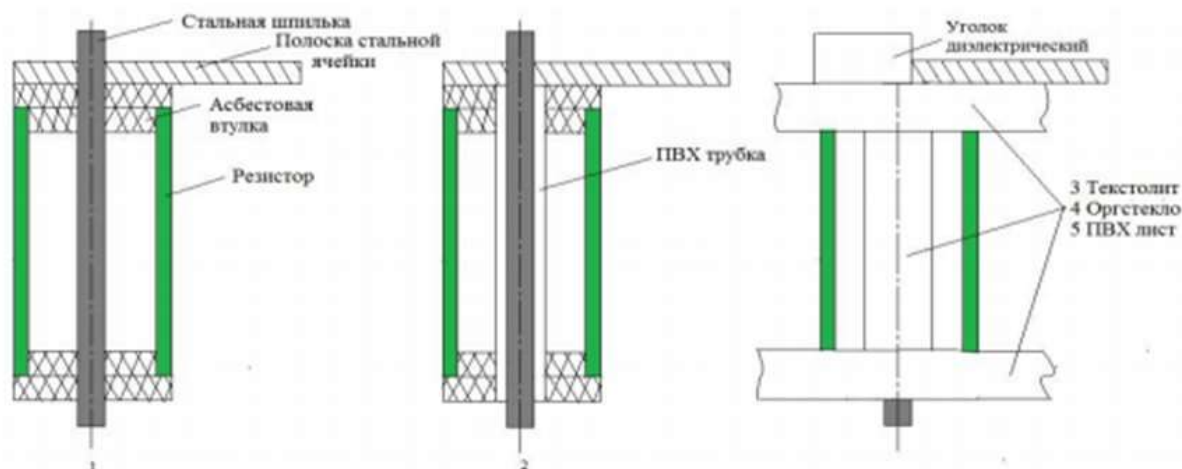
Варианты конструкции и крепления заземляющих резисторов в ячейке ТН
